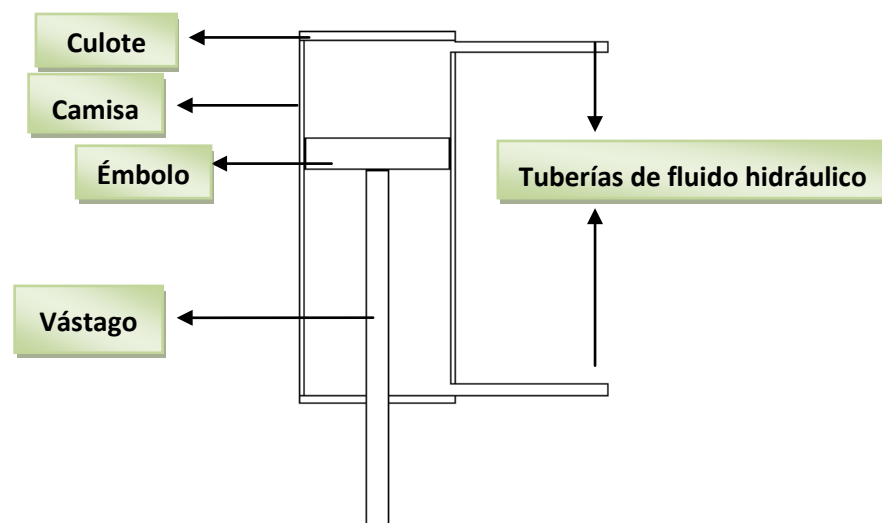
Partes principales de un cilindro hidráulico de doble efecto.
